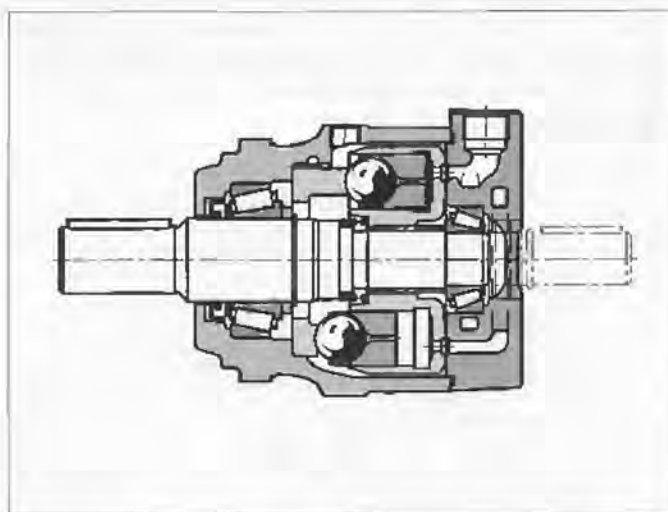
Многотактный аксиально-поршневой гидромотор с неподвижным корпусом
